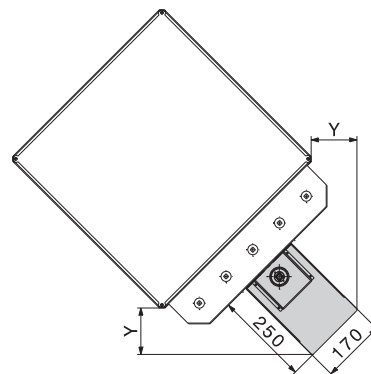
Maßbild Adapter für Krivan /Ausführung S (in mm)
